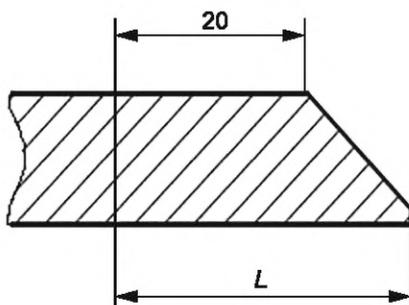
Размер участка контроля присоединительного конца под приварку
